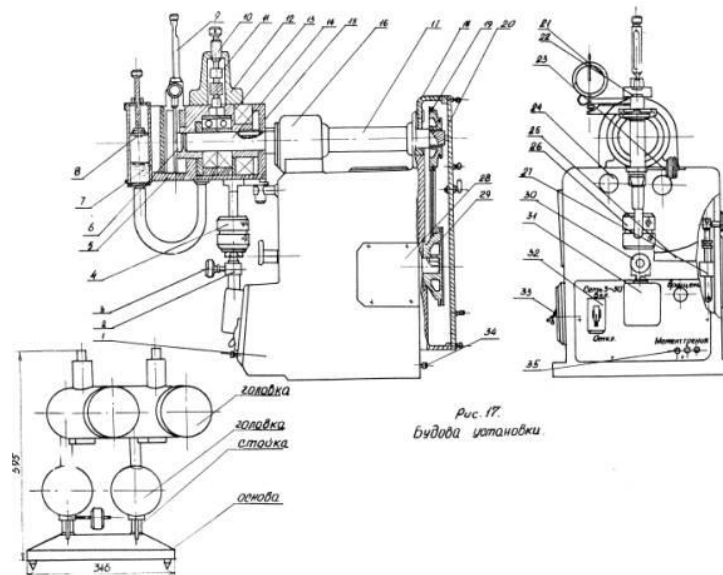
Лабораторна установка для вимірювання моменту тертя у підшипниках
